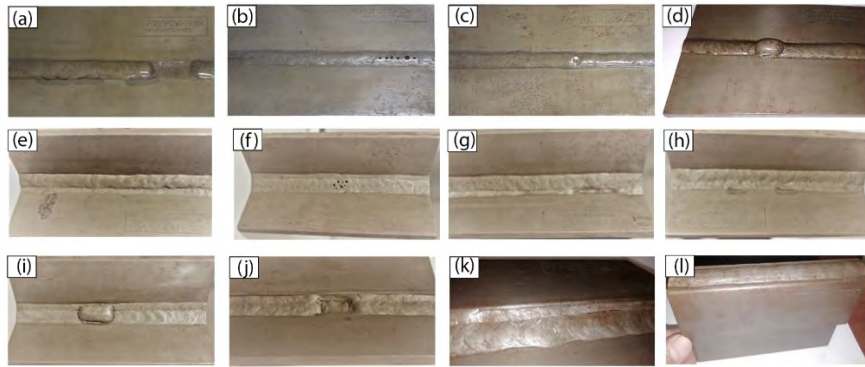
(a, b, c, d) soldadura de ranura junta a tope, (e, f, g, h, i) soldadura de filete junta en T, (j, k) soldadura de filete junta de solape, y (l) soldadura de ranura en junta de borde
